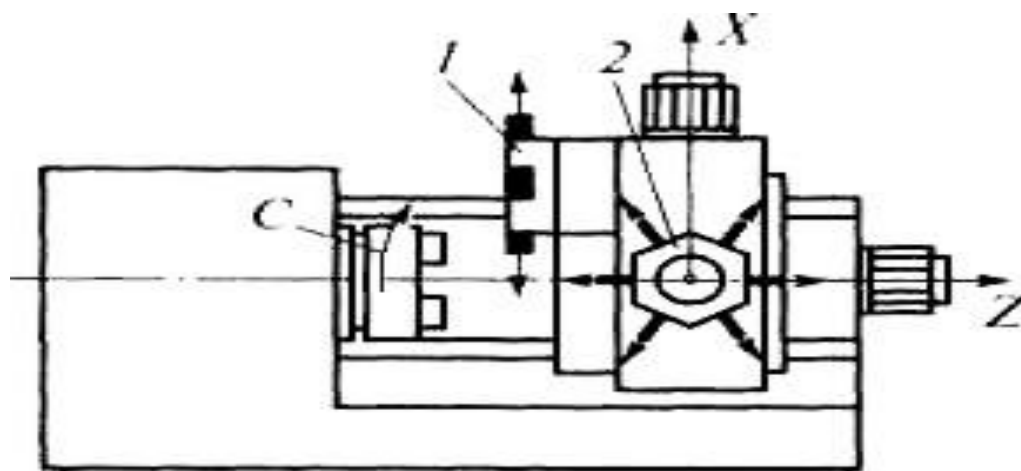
Токарний верстат з ЧПК: 1, 2- револьверні головки
